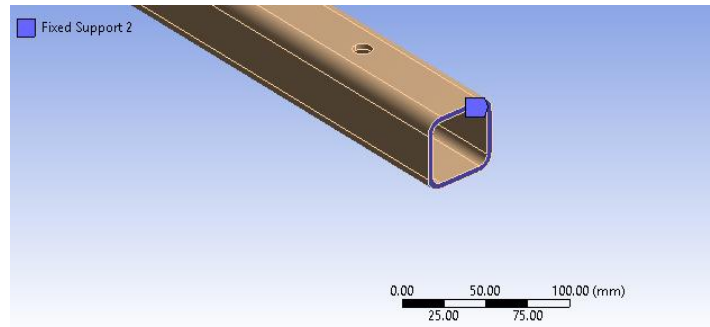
Empotramiento sobre la barra que se une al conjunto pórtico de sujeción.
